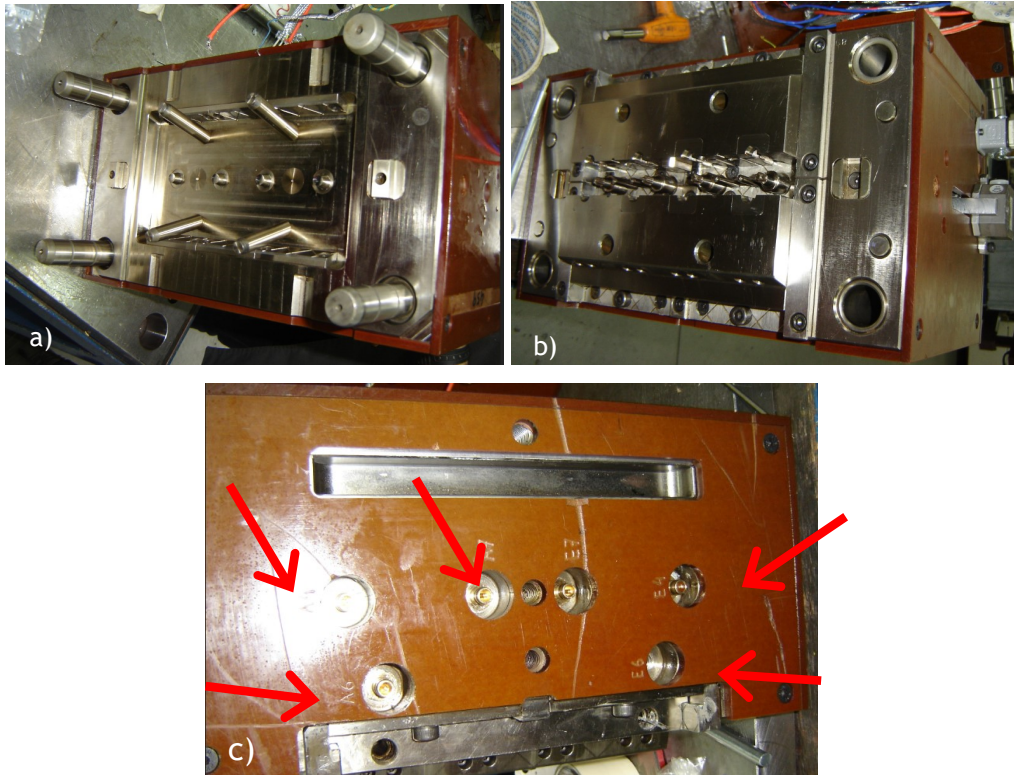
Molde injetado com PEEK. a) Lado Injeção molde injetado em PEEK. b) Lado Extração molde injetado em PEEK. c) Ligações a óleo á máquina injeção.
